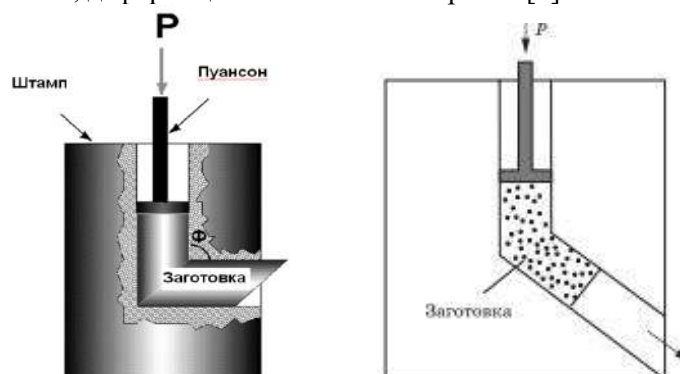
Схема установки РКУП под углами а) 90° б) 120°
